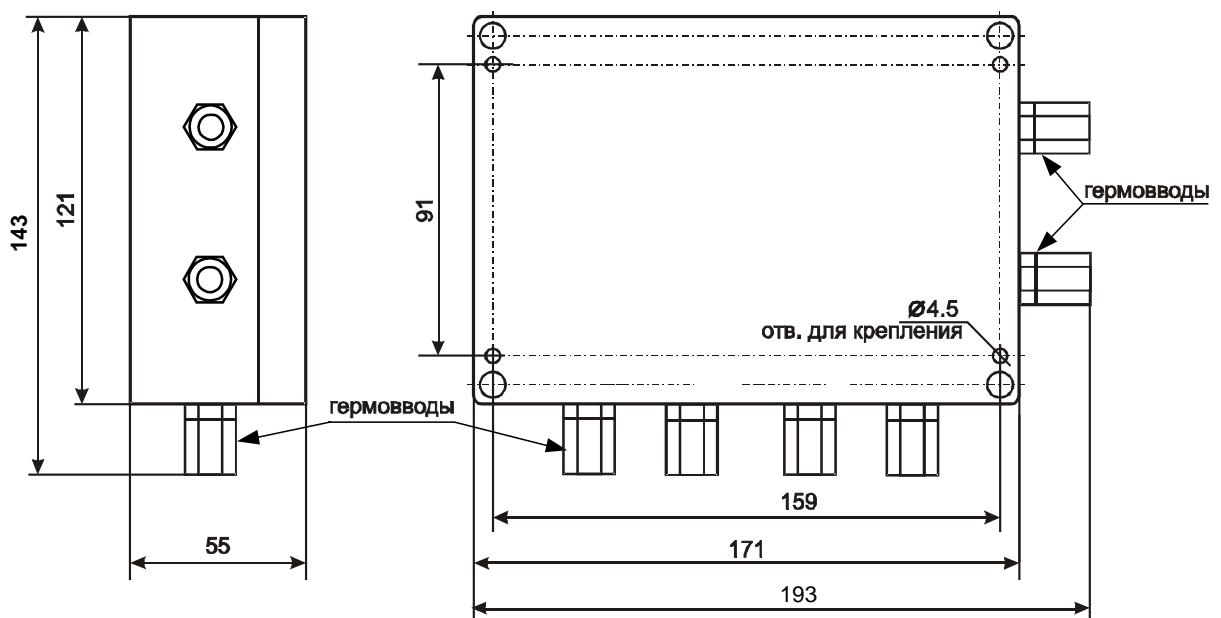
Габаритные и присоединительные размеры СКУ IP65
